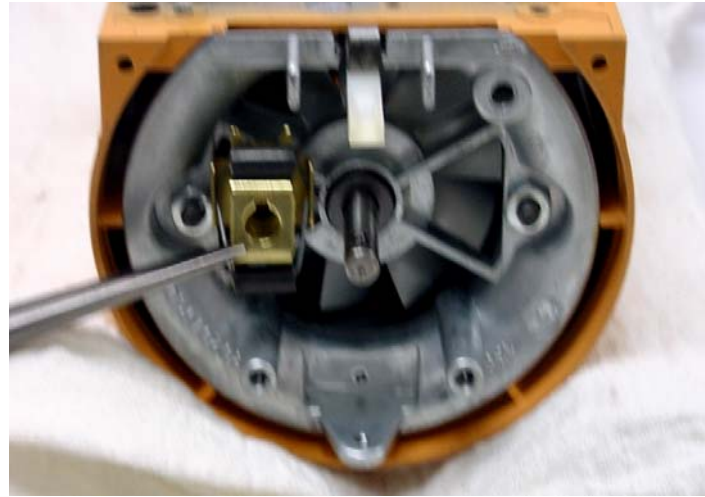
Fliehkraftregler vor dem Aufsetzen auf die Motorwelle.
